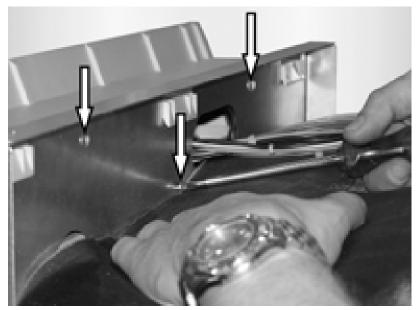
Das Kesselschaltfeld (ohne Regelung) von der Rückseite des vorderen Verkleidungsbleches mit drei Blechschrauben befestigen.
